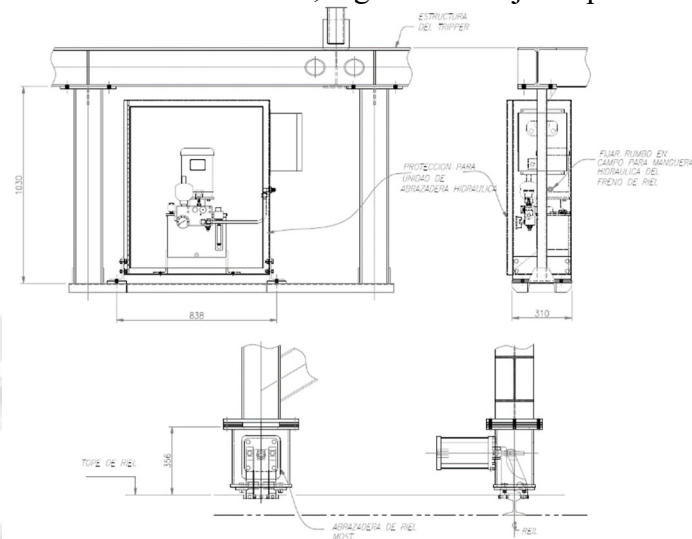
Sistema hidráulico de frenado del Carro descargador (Tripper Car)
